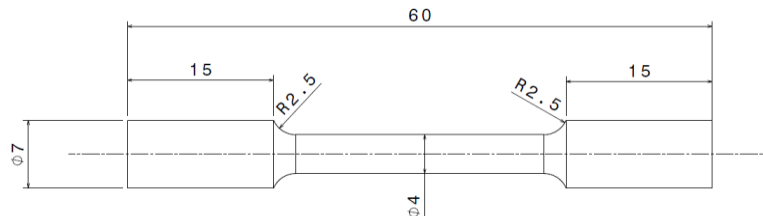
Dimension des éprouvettes des boulons et rivets
